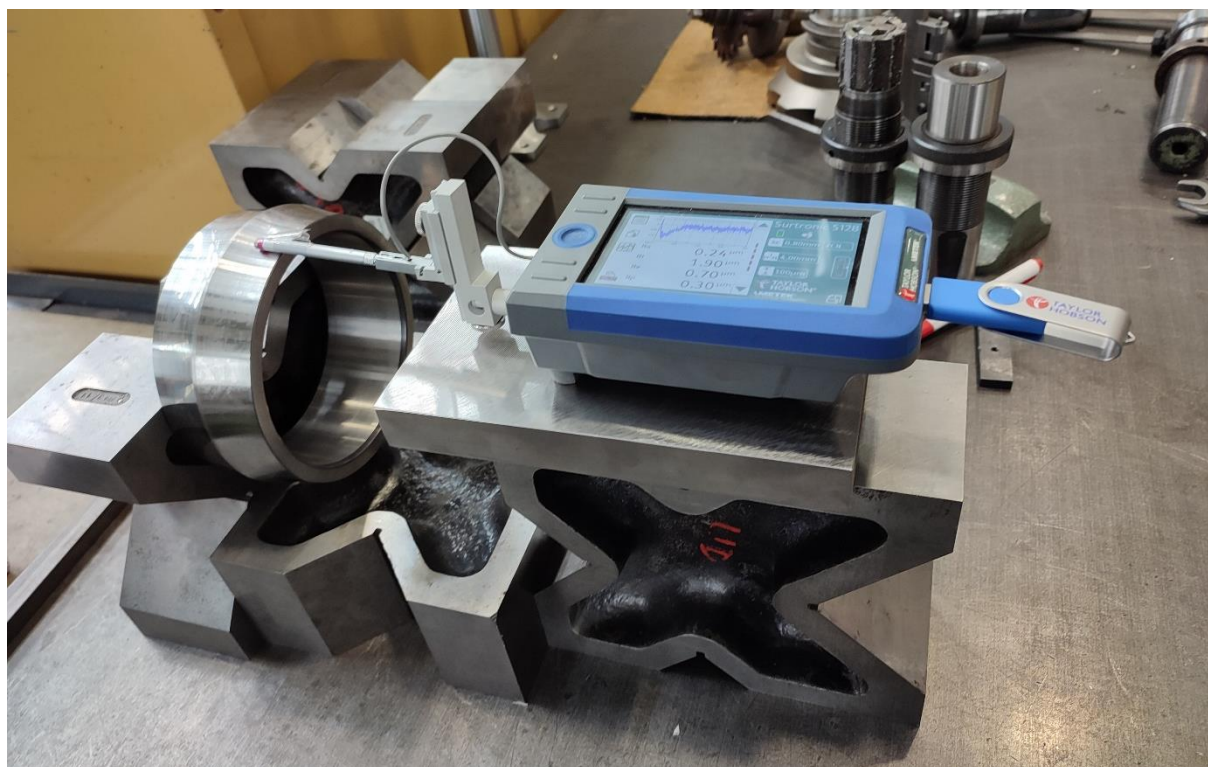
Měření soudečku 23164CJ-3 číslo 5.
